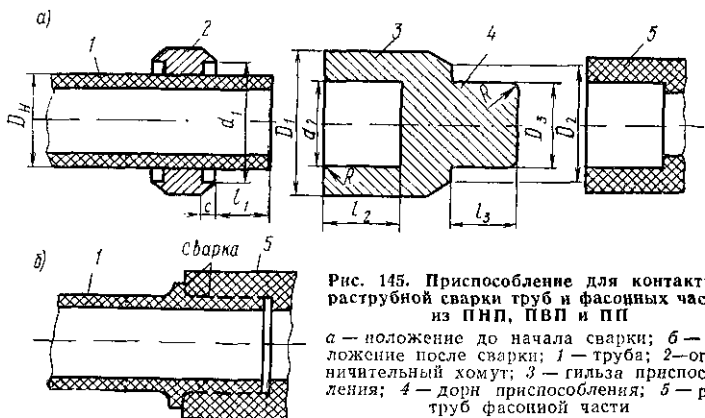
Приспособление для контактной раструбной сварки труб и фасонных частей из ПНП, ПВХ и ПП
